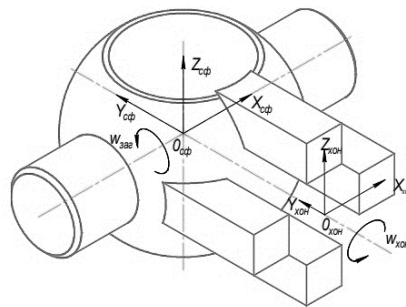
Схема руху інструменту і заготовки при шліфуванні сфери кульового крана [8]
